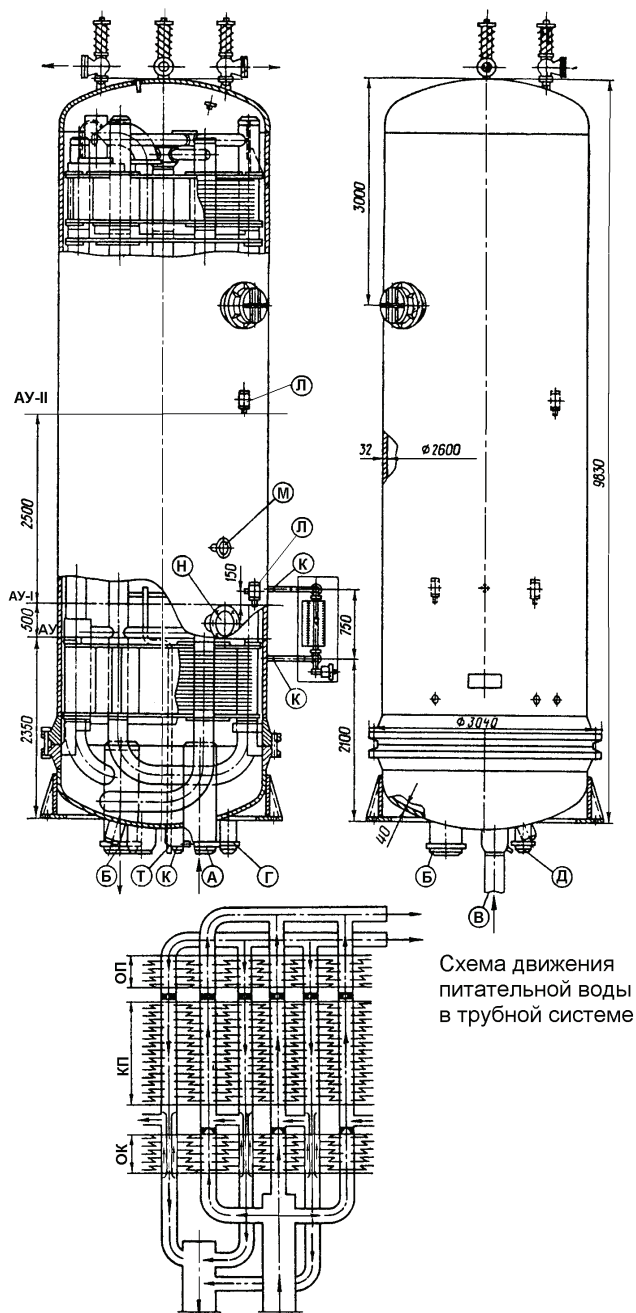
Подогреватель высокого давления ПВ-1250-380-21 [5]:
